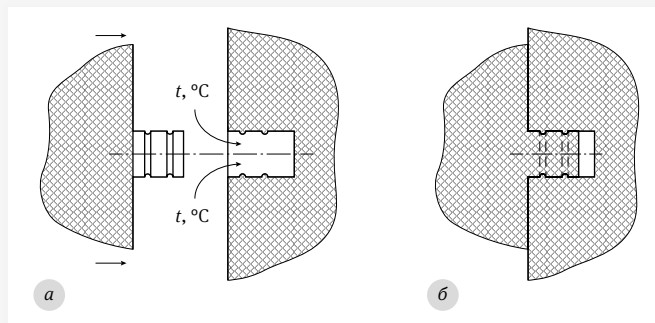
Усовершенствованная сборка модельного блока: а – подготовка к сборке; б – результат сборки
